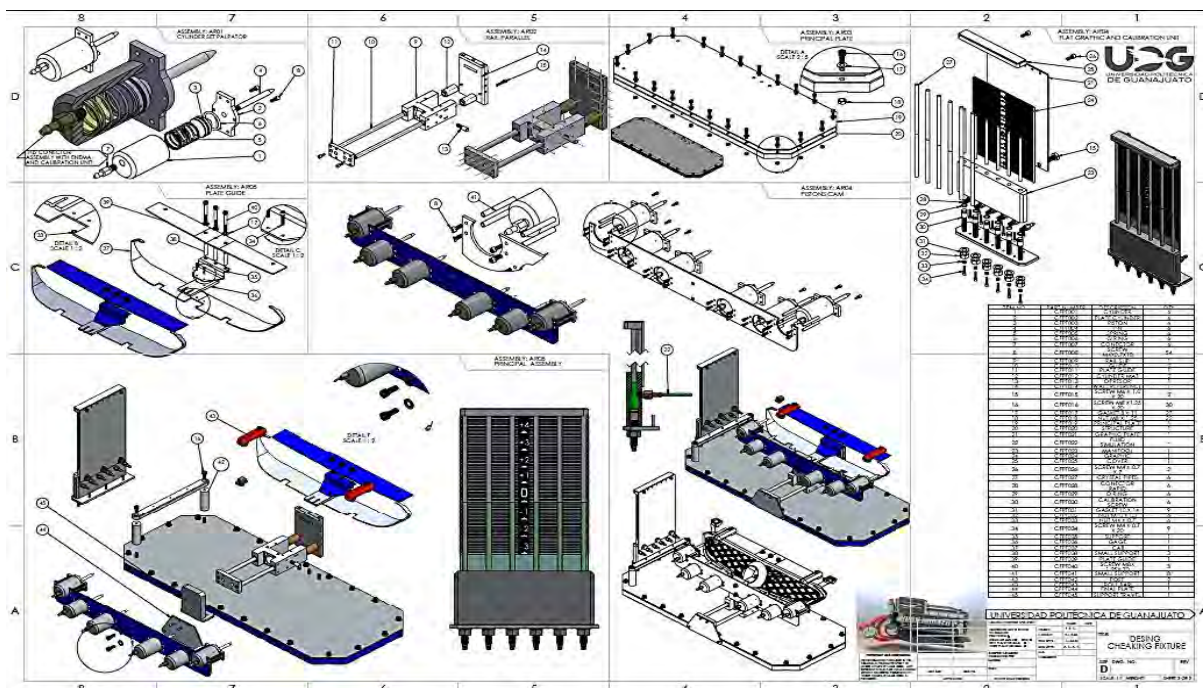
Ensamble final del Checking Fixture modelado en Solidworks 2015.
